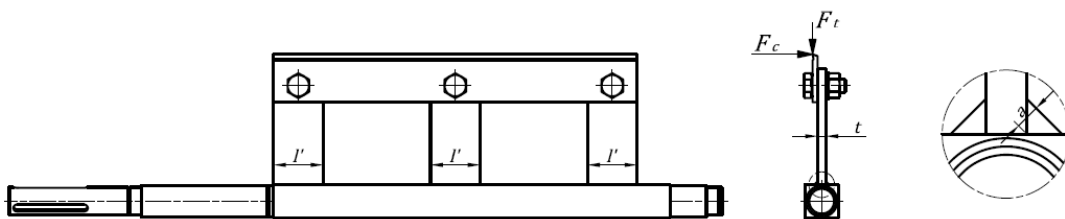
Esquema de la junta soldada entre el árbol y los brazos, muestra además el detalle del cordón de soldadura con sus respectivas dimensiones.
